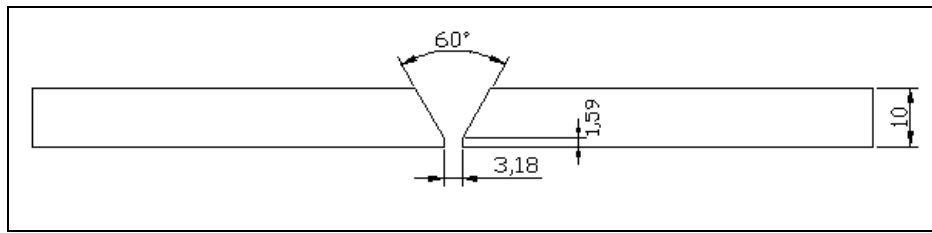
Esquema de diseño de juntas soldadas de acero AISI 1045, dimensiones en mm.
